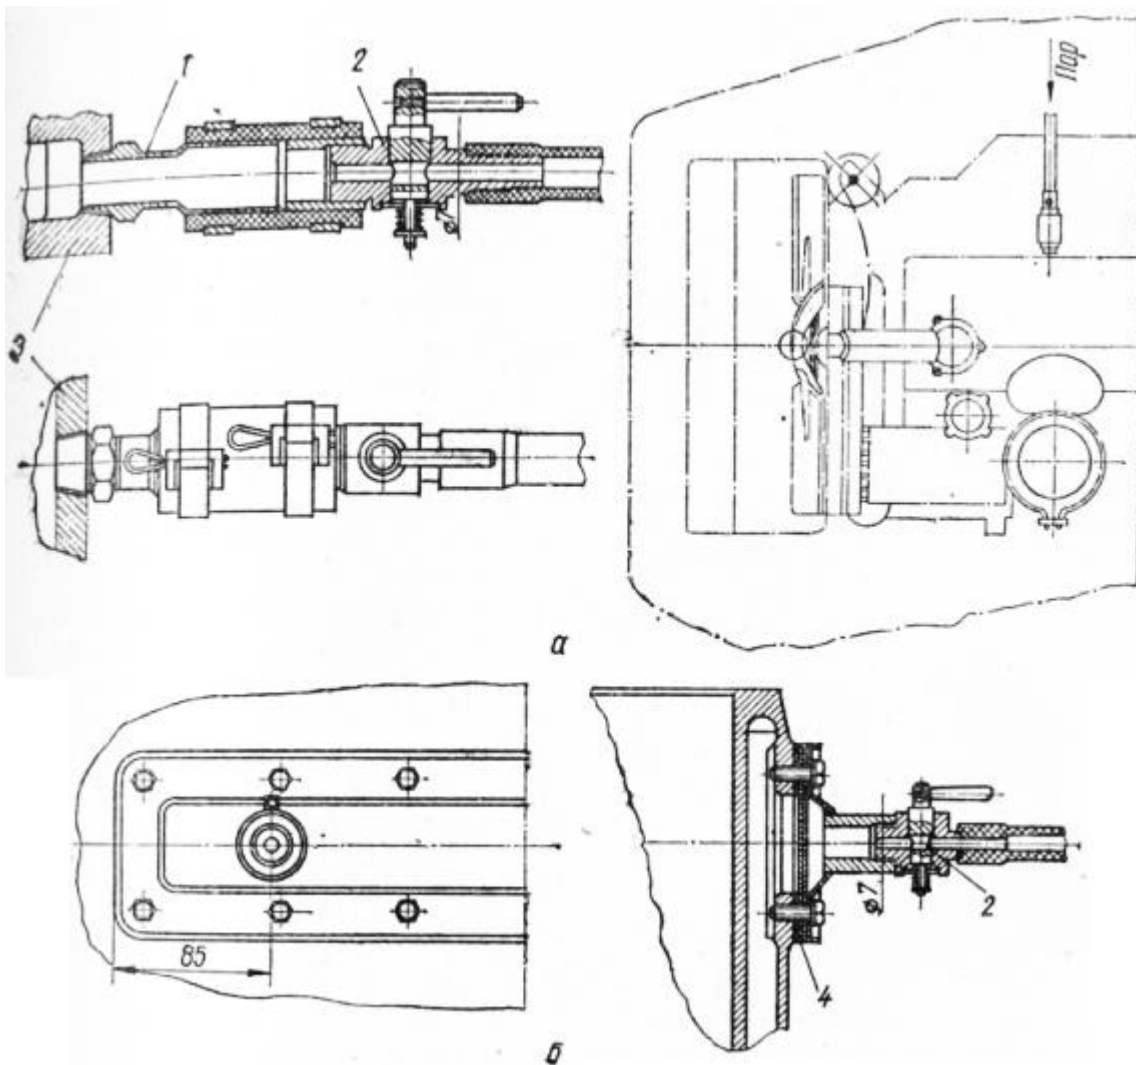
Аппаратура для ввода пара в систему охлаждения при разогреве двигателей: а — ГАЗ-51; б — ЗИЛ-120; 1 — штуцер; 2 — кран; 3 — головка блока; 4 — распределительная пластинка
